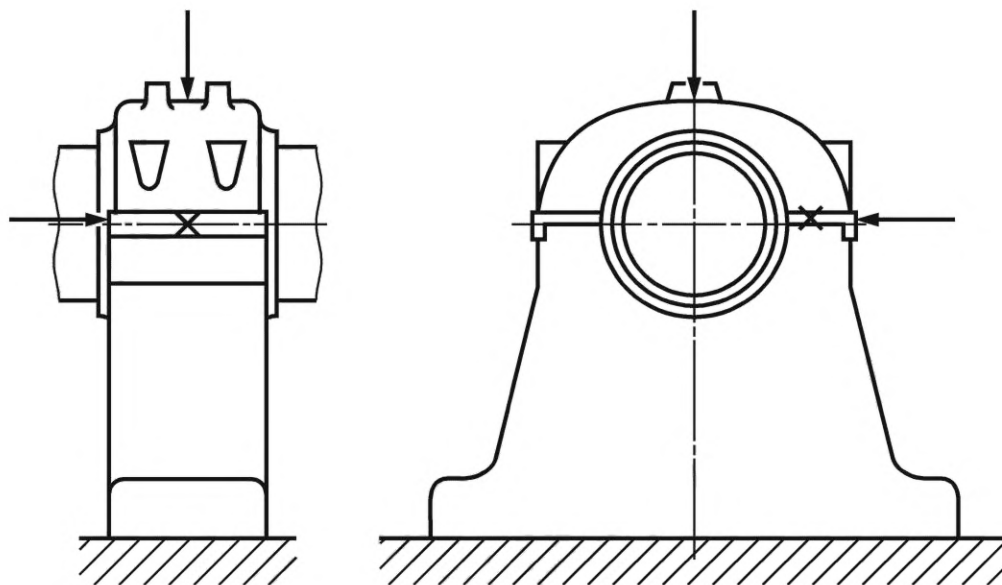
Точки измерений на опорах/крышках подшипников
